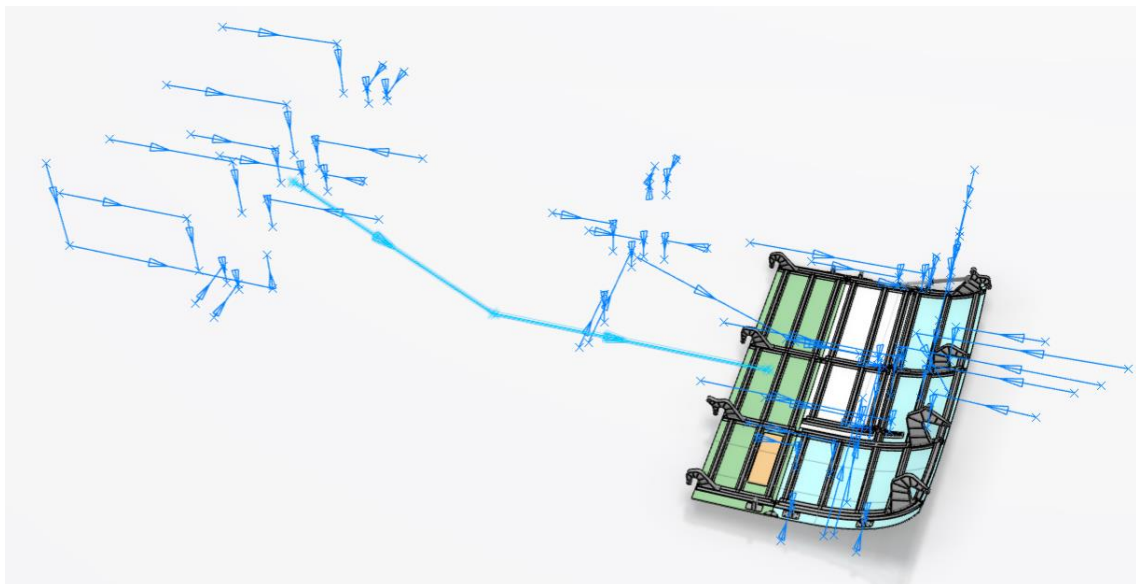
Ensamblaje: Puerta central posicionada. Producto final terminado. Fin del proceso de ensamblaje
